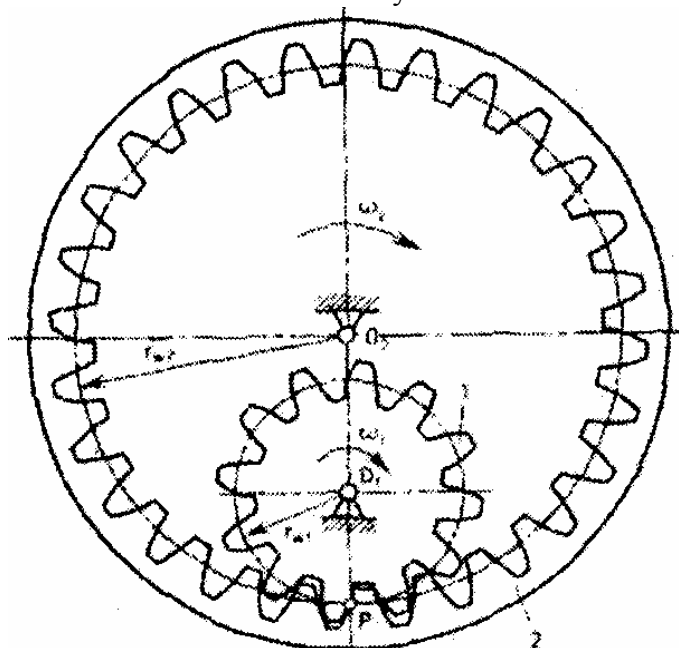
Внутреннее зацепление зубчатых колес
